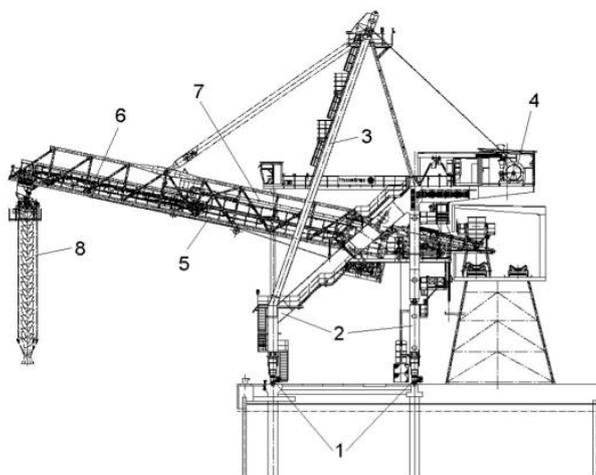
Судопогрузочная машина для погрузки серы. 1 - механизм передвижения; 2 – портал; 3 – пилон; 4 – подъемный механизм; 5 – стрела; 6 – подающая головка; 7 – консольный транспортер; 8 – самотечный спускной желоб
